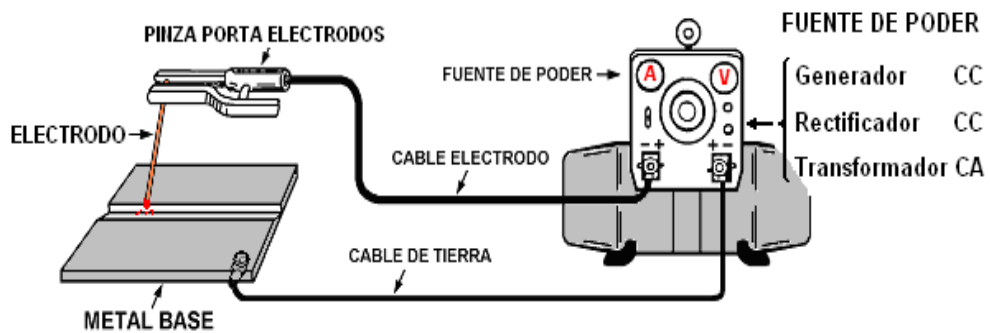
Principios de la soldadura eléctrica al arco SMAW.
